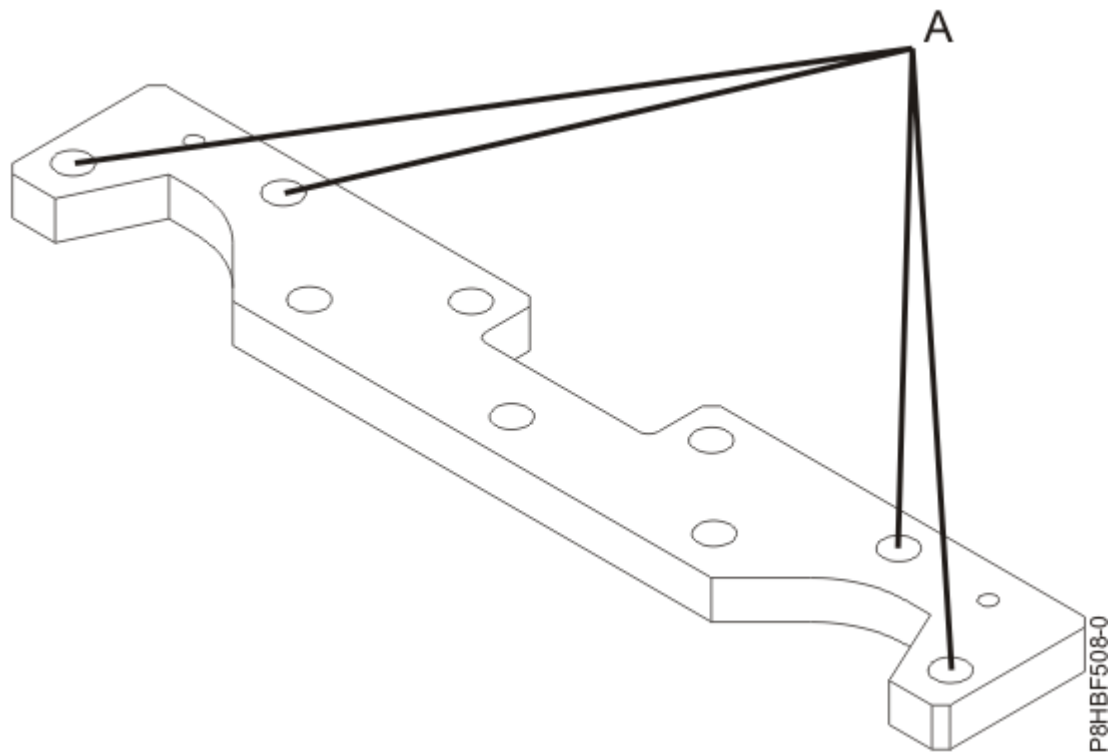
Localizações recomendadas do parafuso inferior para o rack com a chave X
